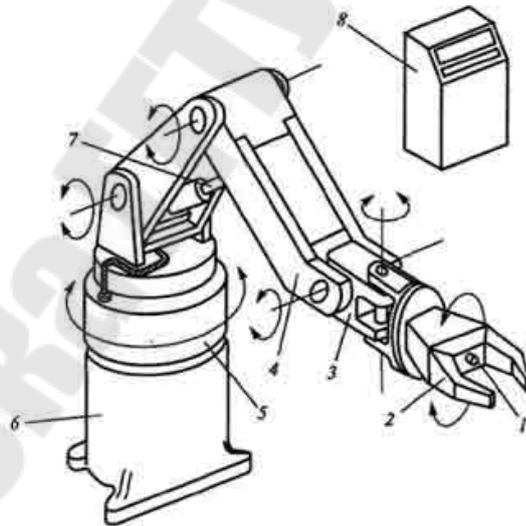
Конструкция промышленного робота: 1 - датчик обратной связи; 2 — захватное устройство; 3 — кисть; 4 — рука манипулятора; 5 — колонна; 6 — несущая конструкция (основание); 7 - привод руки; 8 - блок управляющего устройства с пультом.
